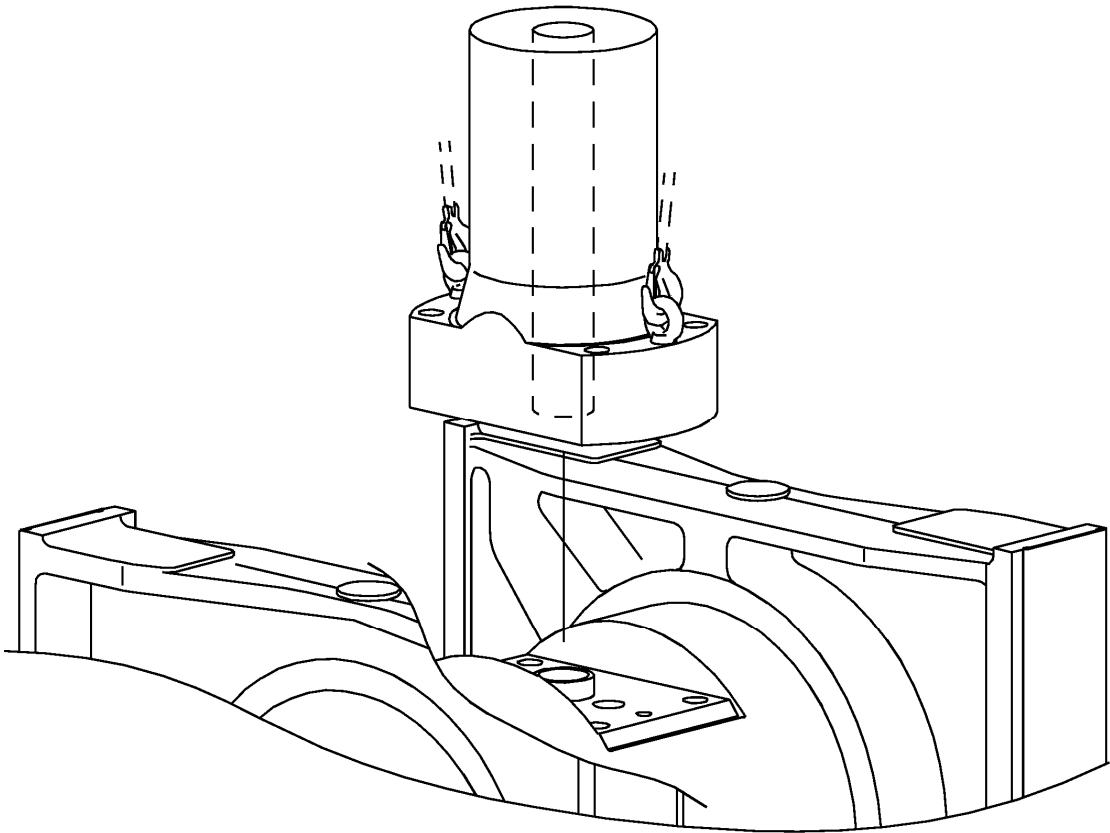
Зняття старої й установка нової регулювальної прокладки
